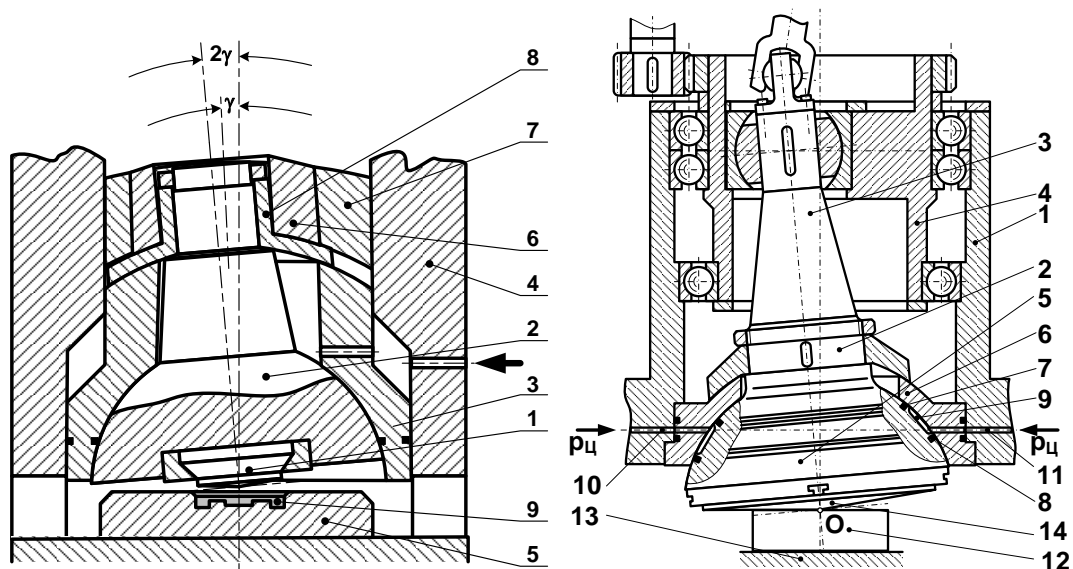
Схема механізму обкочувального руху інструменту [33].
